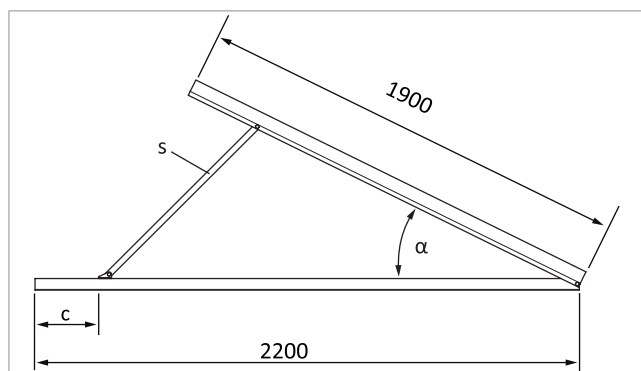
supporti per tetto piano, dimensioni e angolo di inclinazione
